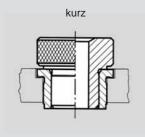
Steckbohrbuchse DIN 173 E kurze Ausführung mit Grundbuchse DIN 173 G
